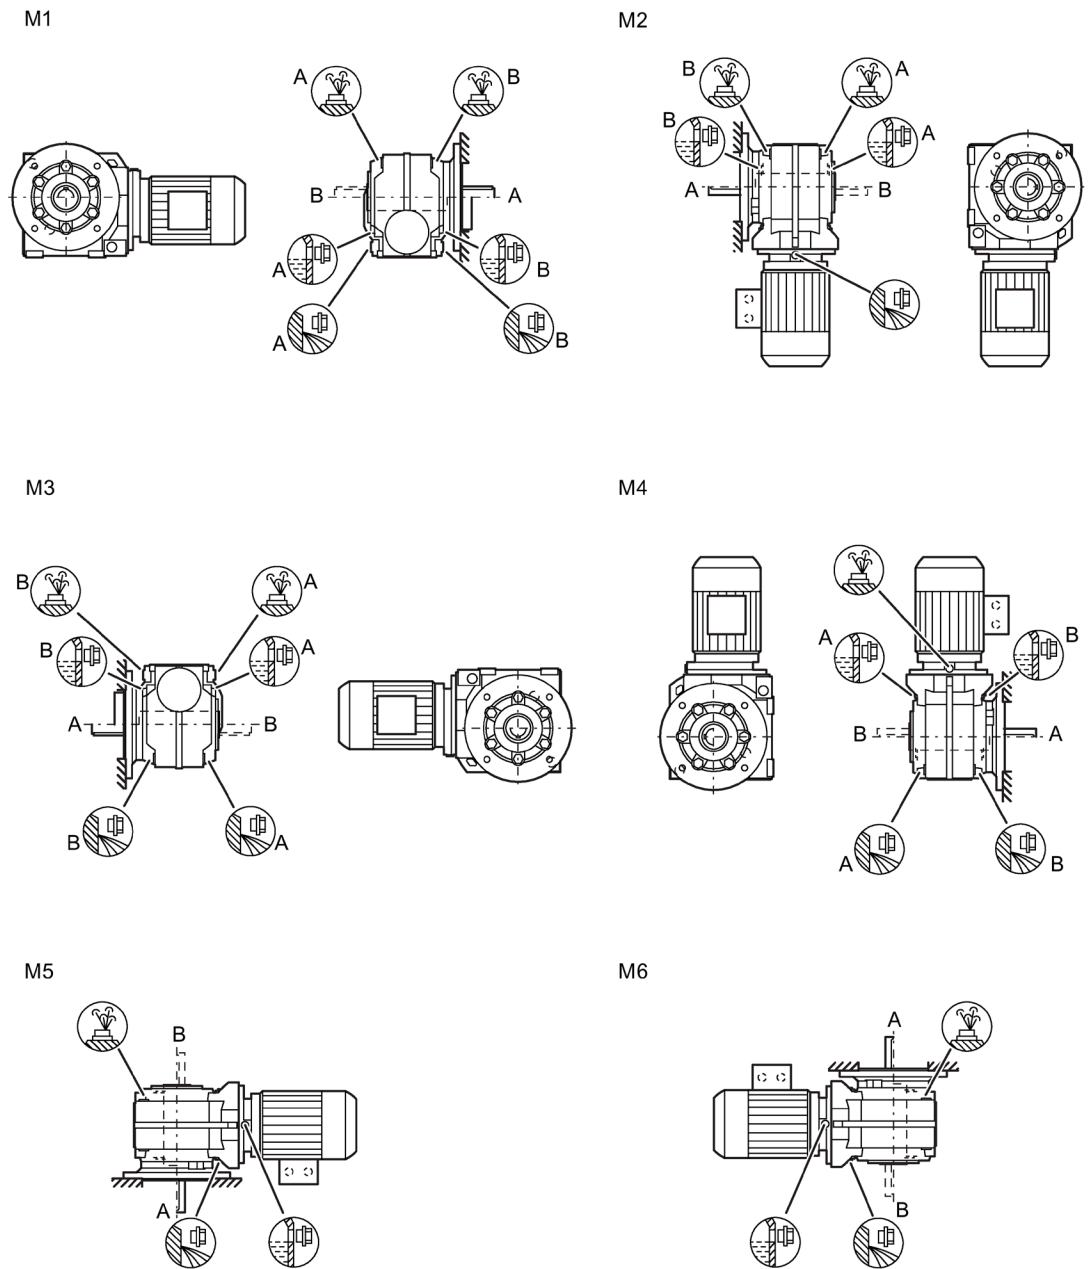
Einbaulagen für Stirnrad-schneckengetriebe CF Flanschausführung und CAZ mit Gehäuseflansch, Baugrößen 39 - 89
